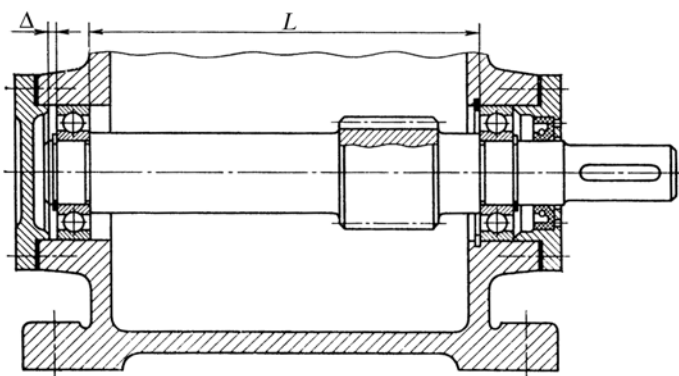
Посадка подшипника на вал до упора в торец.
